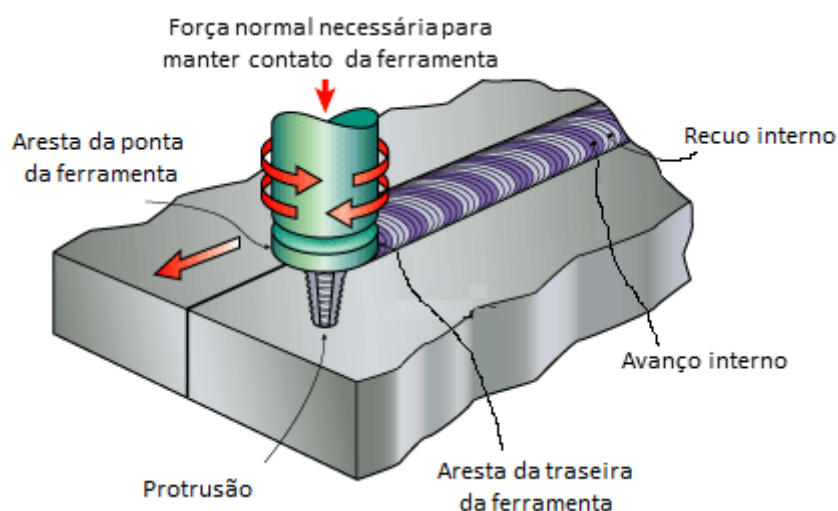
Princípio básico de “Re-stir” - mostrando a técnica de inversão.
